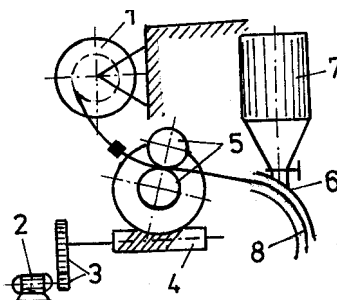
Aparat de încărcare cu sudură sub strat de flux*: 1-bobină pentru sârmă; 2-electromotor; 3-roți dințate; 4-angrenaje melcate; 5-role pentru avansul sârmei; 6-conductă cu ajutor; 7-buncăr pentru flux; 8- diuză
